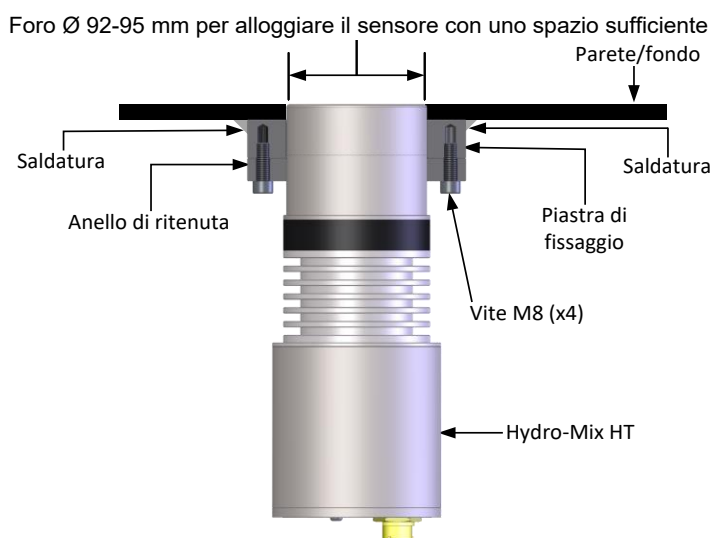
Installazione del sensore (piastra di fissaggio montata esternamente)
